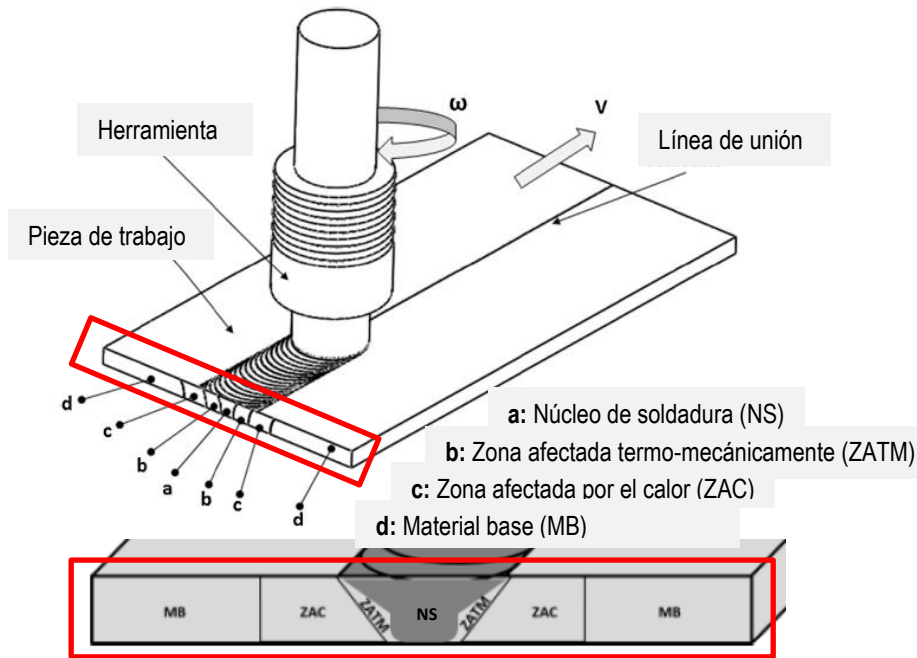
Esquema de la técnica de soldadura por fricción y agitación y de las zonas que conforman en cordón de soldadura [9].
